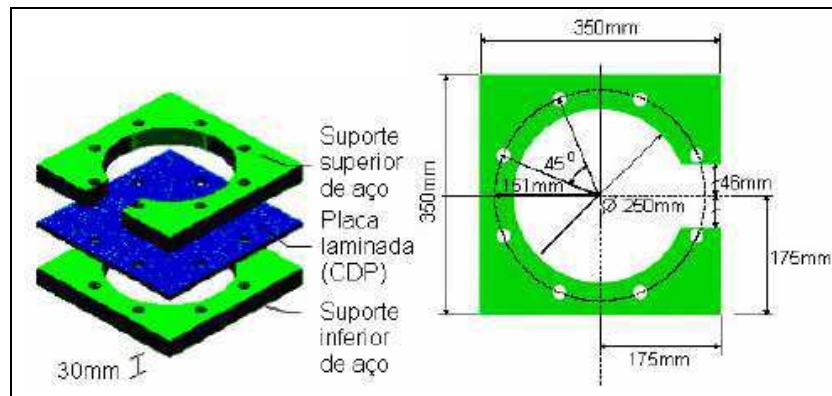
Dimensões do corpo de prova e os suportes rígidos de fixação com parafusos.
